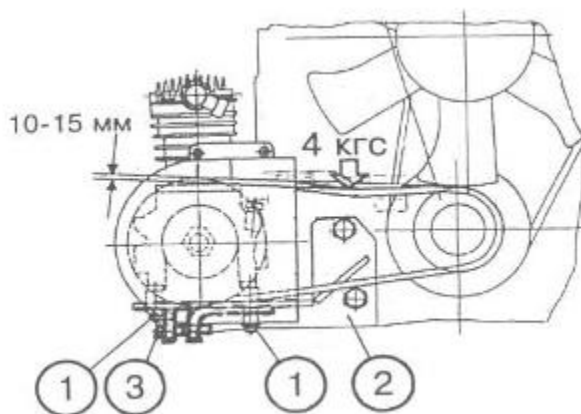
Проверить натяжение ремня привода компрессора.
